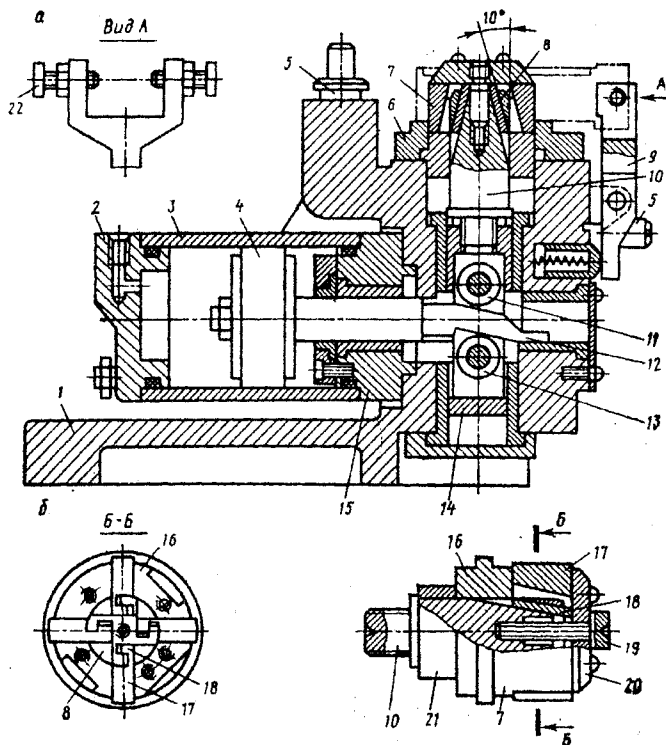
Пристрій для закріплення заготовок на агрегатному верстаті
